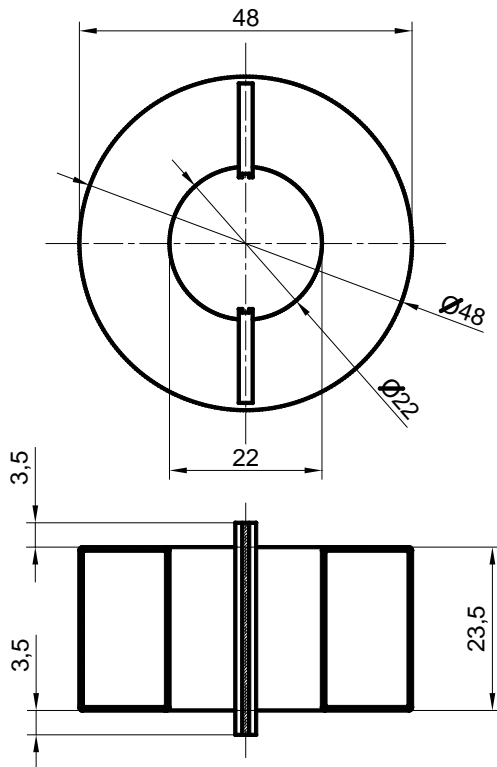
Внешний вид и габаритные размеры магнитопровода MSFN-45S-TH1
